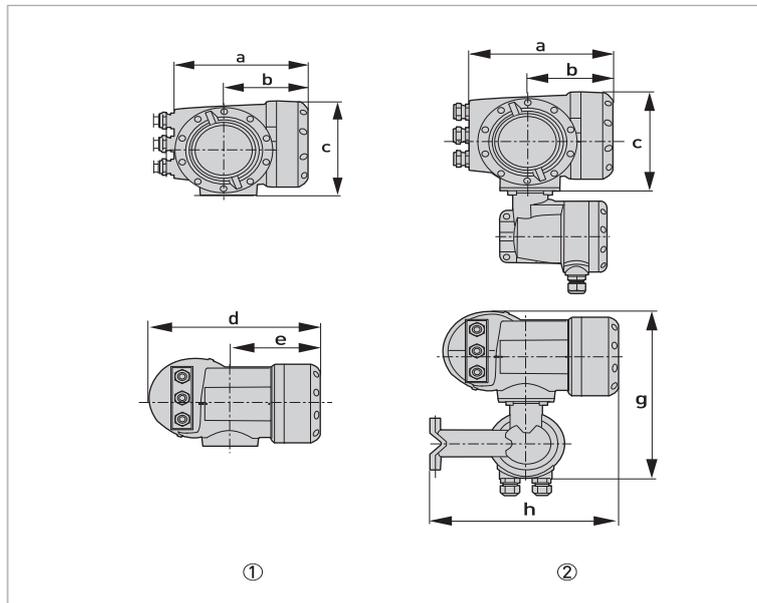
Габаритные размеры корпуса преобразователя сигналов
